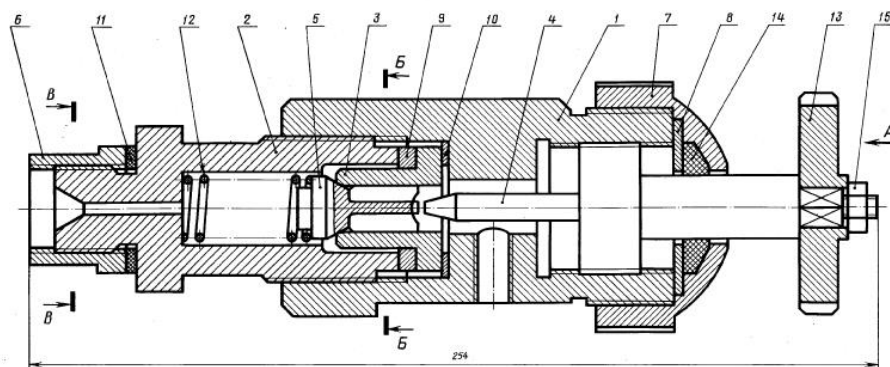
Чертеж выключателя подачи топлива дизеля, где цифрой 1 обозначен корпус
